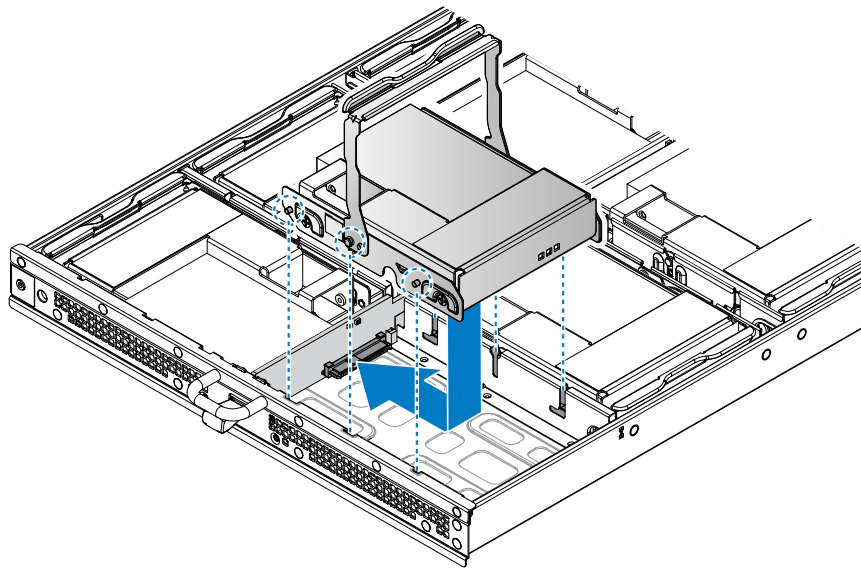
Installation de l'assemblage de disque dur de 2,5 pouces
